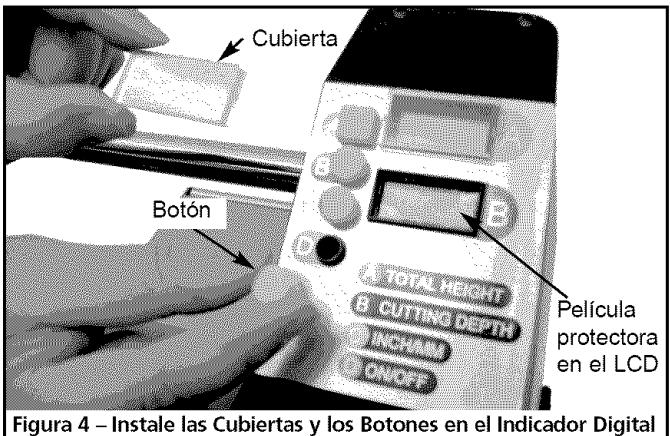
Instale las Cubiertas y los Botones en el Indicador Digital
